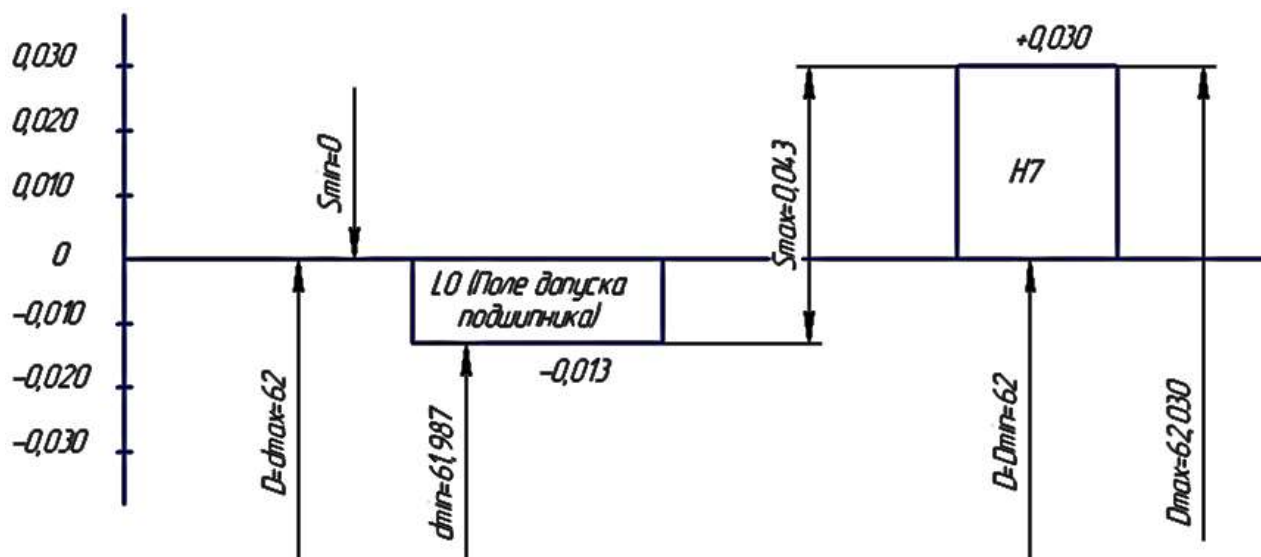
Графическое изображение полей допуска подшипника и отверстия корпуса.
